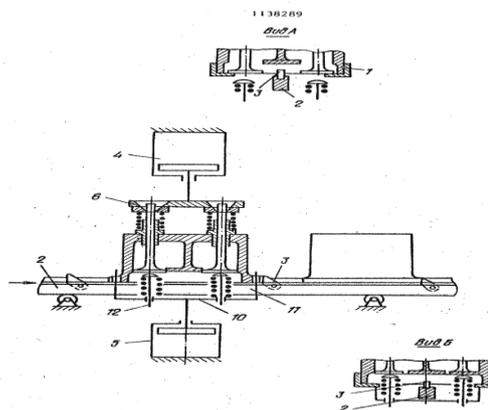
Стенд для сборки и разборки головок блоков цилиндров двигателей
